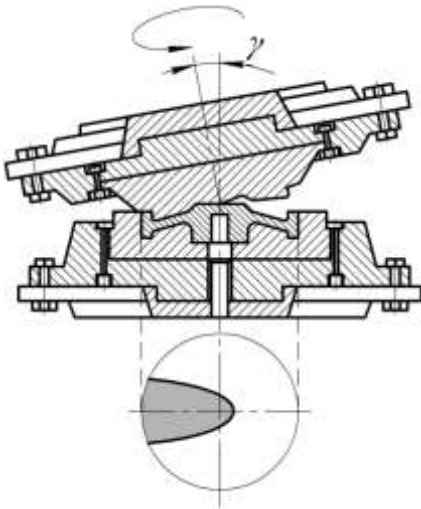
Схема виробництва коліс сферорухомим пресувачем
